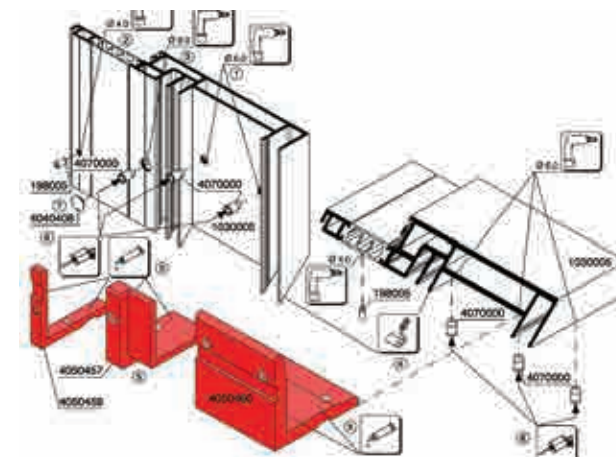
Escuadras para el ensamblaje de perfiles.
